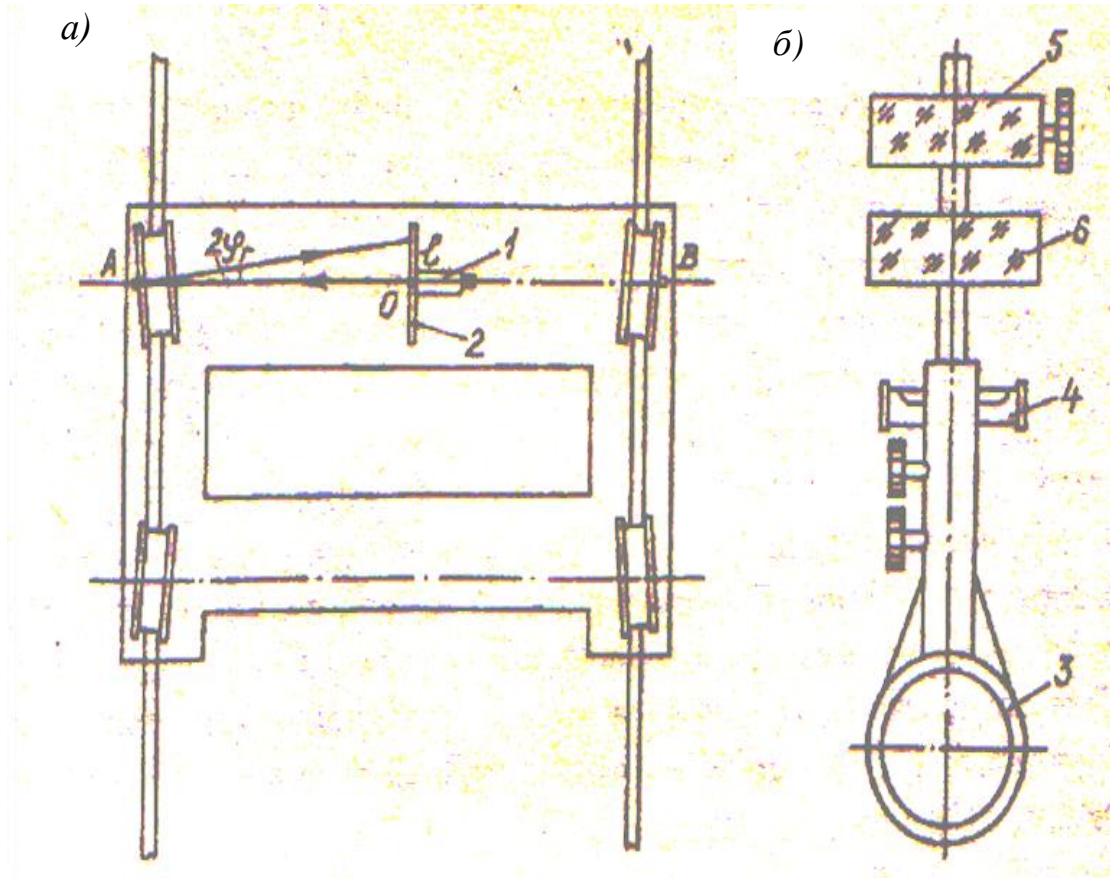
Схема устройства (а) и стойка с опорной пластиной и зеркалами (б)
